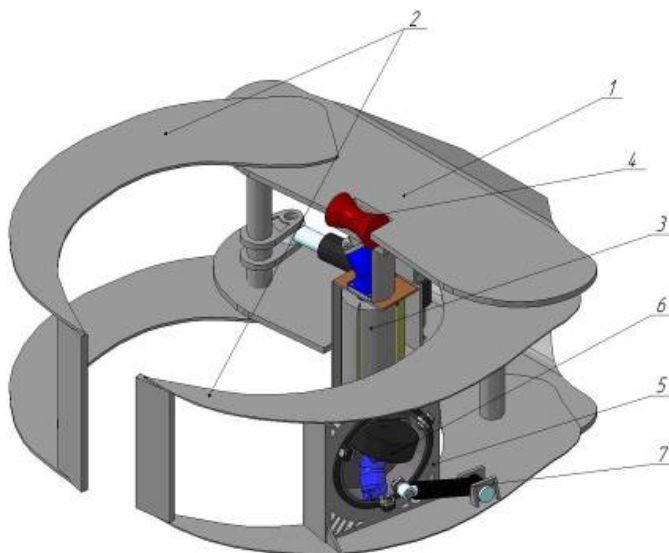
Схема модернизированного грейферного захвата форвардера: 1 – корпус; 2 – захваты; 3 – фреза для оцилиндровки закомелистости с приводом; 4 – опорный направляющий валец; 5 – площадка для размещения привода подачи бревна; 6 – гидромотор привода подачи бревна; 7 – гидроцилиндр поворота привода.
